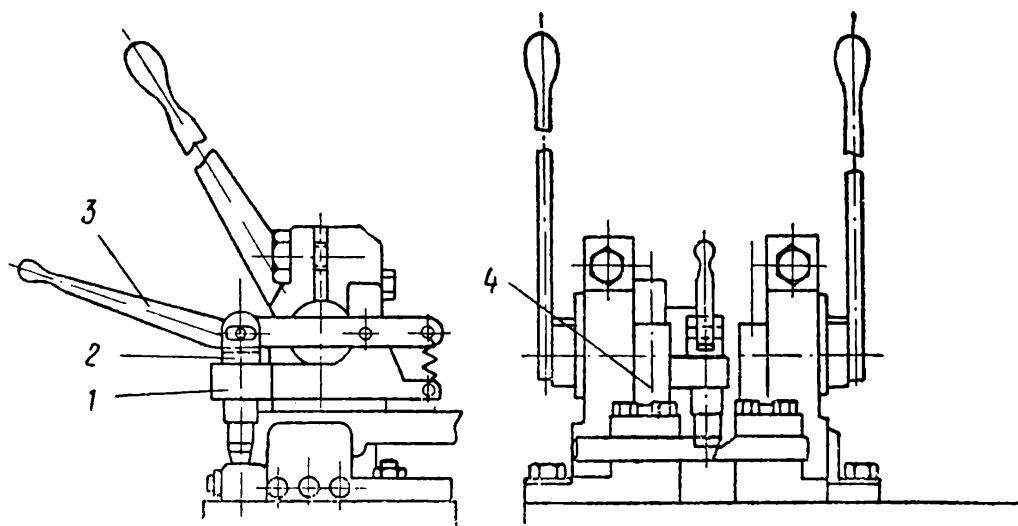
Приспособление к точечной машине МТП-75-5-1 для напайки пластинок на резцы.
